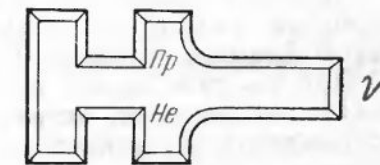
Калибр для контроля геометрических размеров замыкающей головки заклепки
